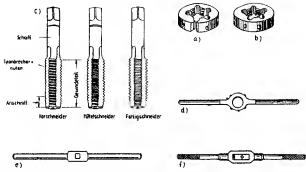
Gewindeschneidwerkzeuge; offenes Schneideisen (o), geschlossenes Schneideisen (b), ein kompletter Satz Gewindebohrer (c). Schneideisenhalter (d), Einlochwindeisen (e) und verstellbares Windeisen (f) für Gewindebohrer
